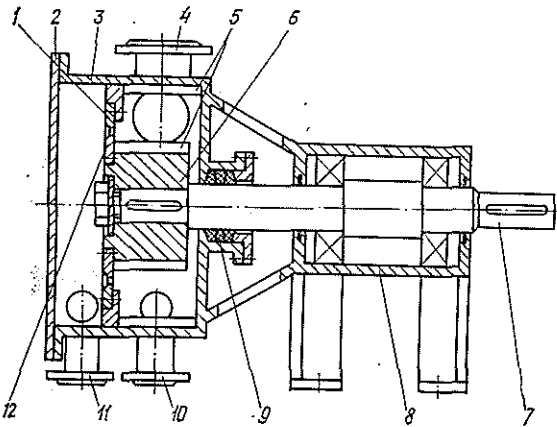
Экспериментальная роторная сортировка: 1 — кольцевая перегородка; 2 — крышка; 3 — корпус; 4 — патрубок для подвода исходной суспензии; 5 — ребро; 6 — ротор; 7 — вал; 8 — опора ротора; 9 — уплотнение; 10, 11 — патрубки для отвода сортированной суспензии и отходов соответственно; 12 — кольцо ротора
